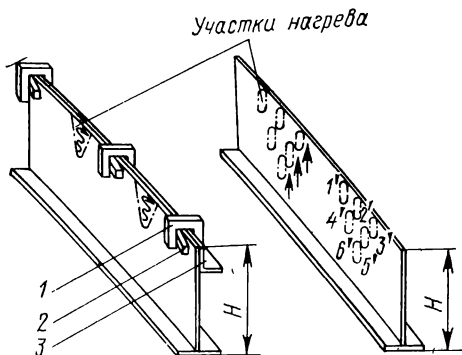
Схема правки сварных тавровых балок с высокой стенкой.
